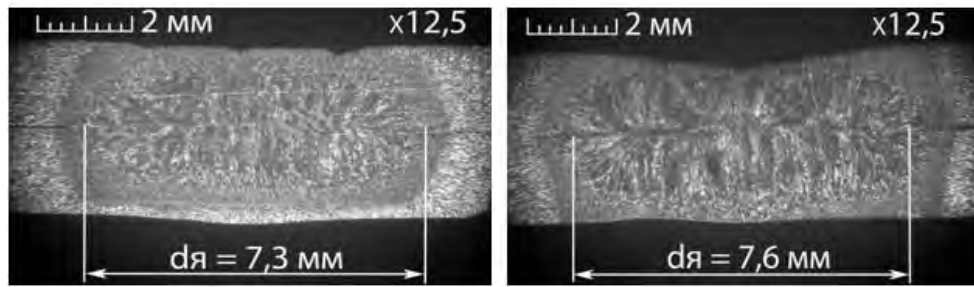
Макрошлифы рельефных сварных соединений двух пластин из стали 08кп толщиной (2 + 2) мм при сварке по одному круглому выштампованному рельефу
